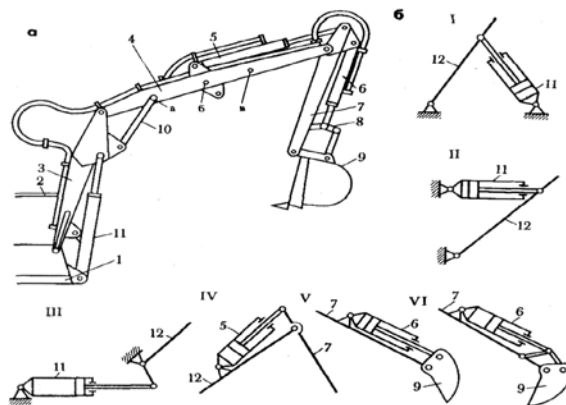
Обратная лопата (а) и схемы расположения гидроцилиндров ее рабочего оборудования (б) для привода стрелы (I...III), рукояти (IV) и ковша (V и VI):
